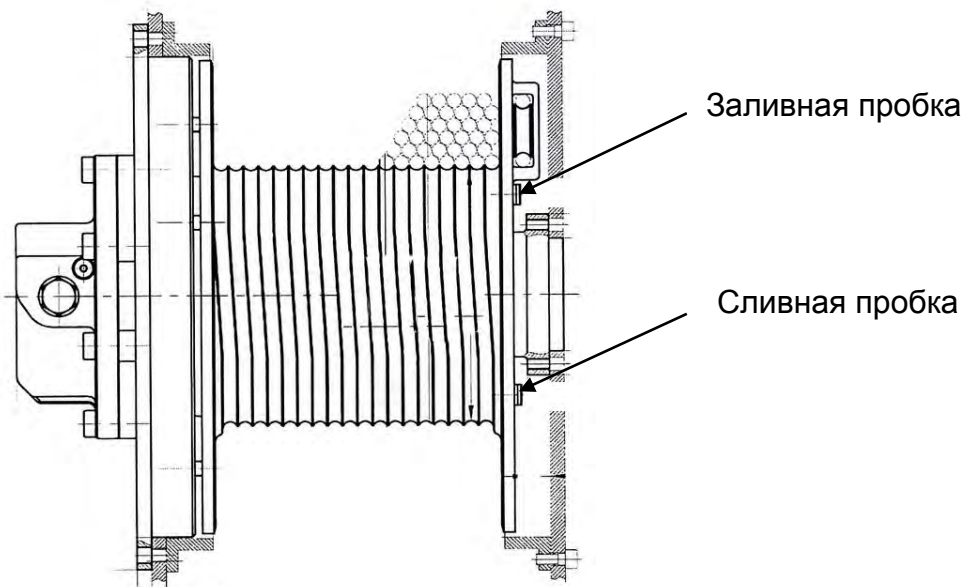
Лебедка с расположением сливной и заливной пробок на боковой (торцевой) поверхности барабана
